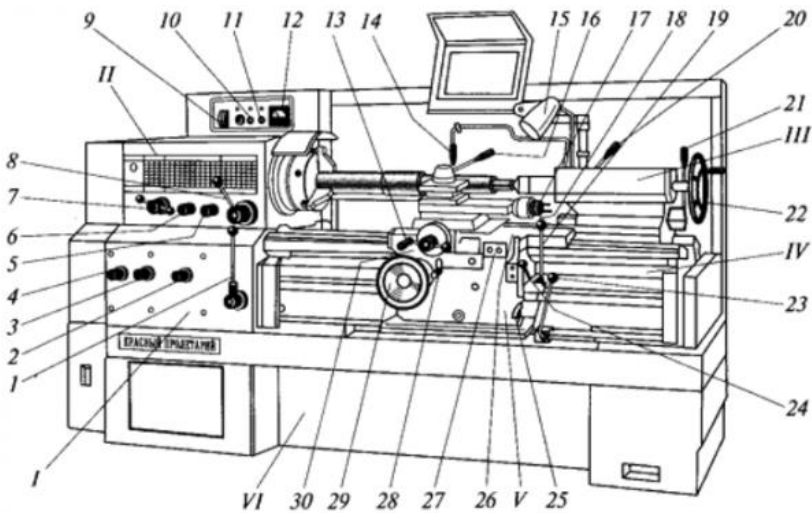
Типовая конструкция токарно-винторезного станка
